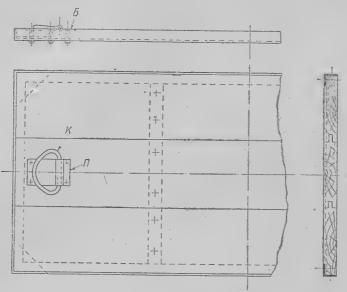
Крышка Глюка: K — кольцо люка, Π — металлическая планка для крепления кольца и крышка люка, B — болты, крепления.
